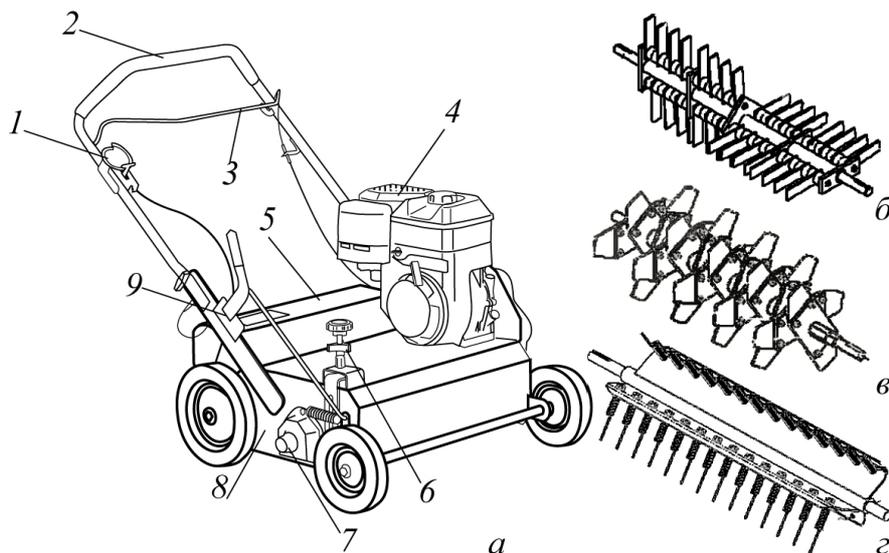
Скарификатор «Husqvarna DT-22» (*a*) с высевающим приспособлением и его рабочие органы (*б-г*): 1 – рычаг привода высевающего приспособления; 2 – рукоятка; 3 – рычаг включения рабочих органов; 4 – двигатель; 5 – высевающее приспособление; 6 – регулировочный винт глубины обработки с блокиратором; 7 – ведущий вал; 8 – корпус; 9 – рычаг перевода в транспортное положение
